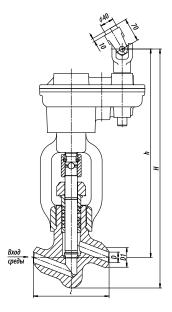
Клапан запорный DN32-65 с циллиндрическим редуктором
